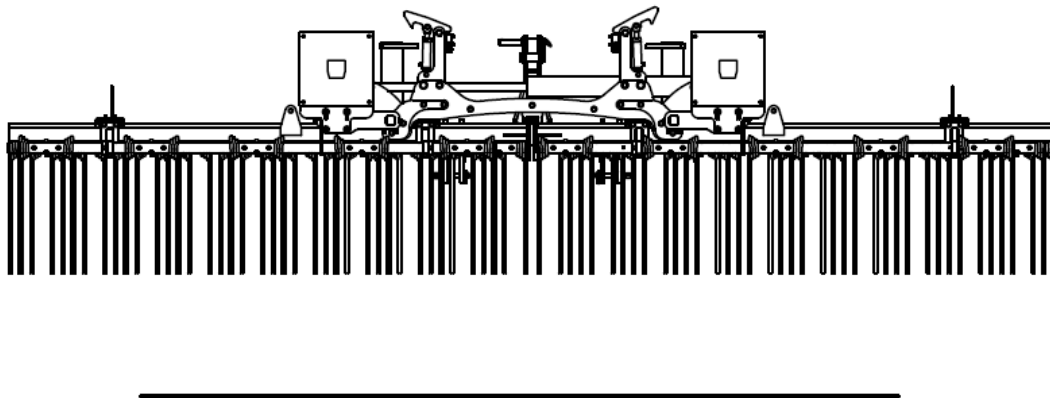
Vue de la machine à la fin de la séquence d'ouverture des ailes. Les bras de la machine sont complètement ouverts.
